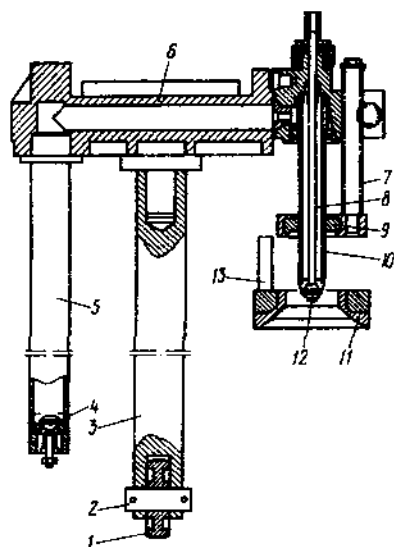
Фасовочное устройство агрегата Girmini 24/6:
